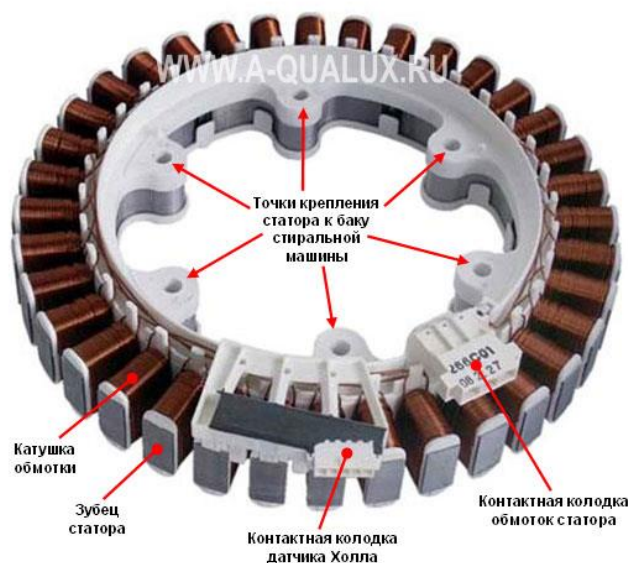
Двигатель стиральной машины, устройство статора
